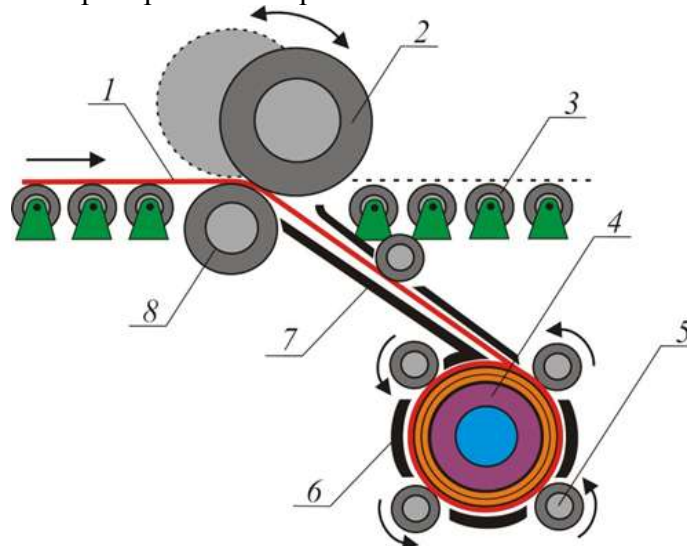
Схема ролико-барабанной моталки: 1— горячая полоса; 2, 8— подающие ролики; 3— рольганг; 4— барабан; 5— формирующий ролик; 6, 7— проводки
